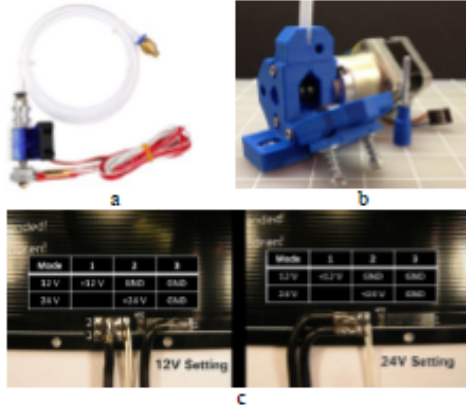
Herramienta de extrusión: a) Extrusor de material, b) Alimentador de material, c) Cama caliente.
